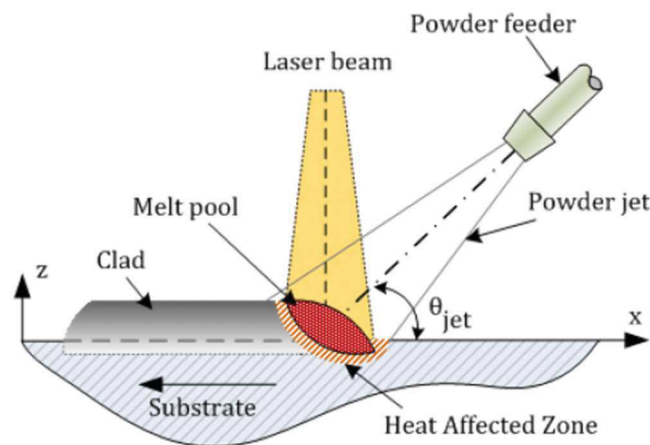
Principe de la fabrication additive par Laser Engineering Net Shaping (LENS) [17].
